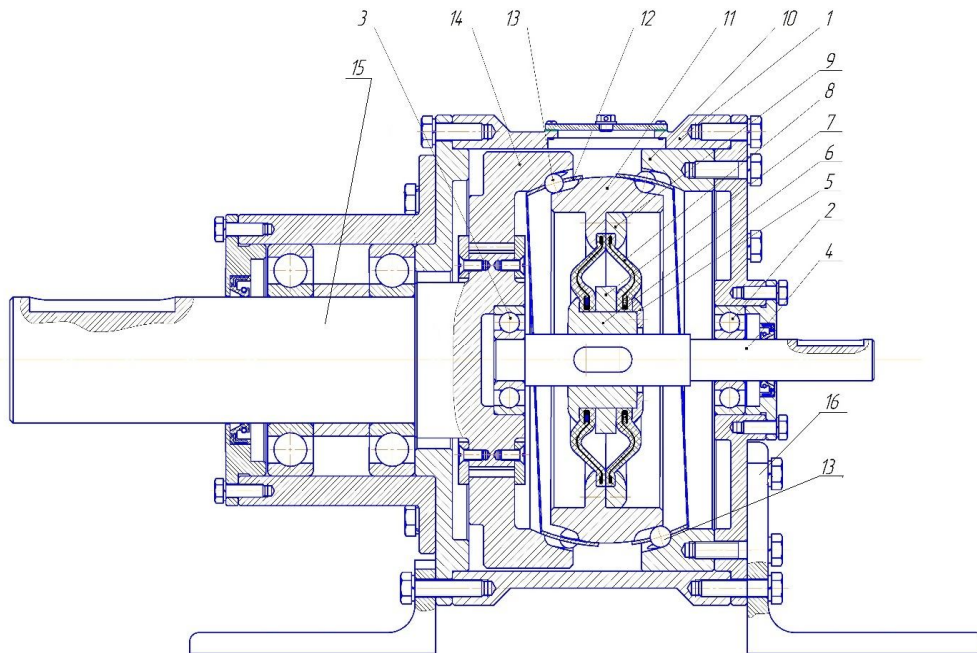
Конструктивная схема разработанной ВППТК: 1 – корпус; 2, 3 – подшипники качения; 4 – ведущий вал; 5 – фланец; 6 – втулка; 7 – промежуточное кольцо; 8 – упругая оболочка; 9 – фланец прецессионного колеса; 10 – неподвижное колесо; 11 – прецессионное колесо; 12 – сепаратор; 13 – тела качения (шарики); 14 – неподвижное колесо; 15 – выходной вал; 16 – опоры
